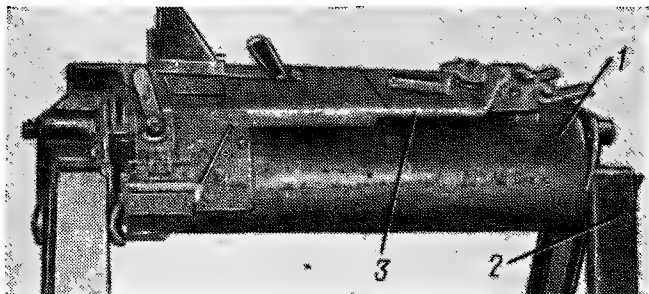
Горбыль для формовки меди катушек неразрезной обмотки:
